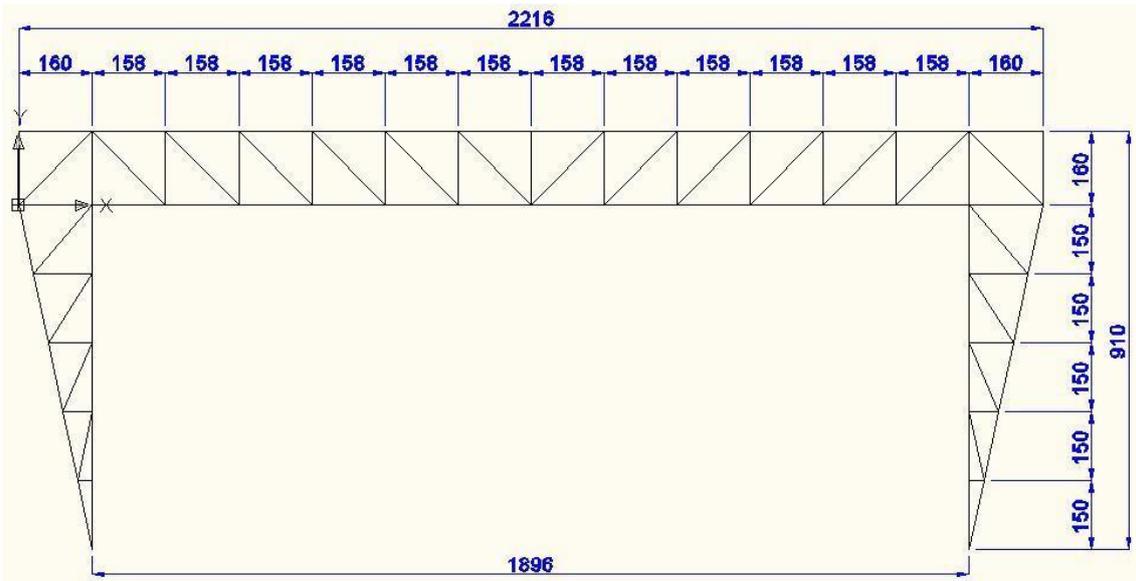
Vista Frontal e dimensões da ponte rolante (em cm)
